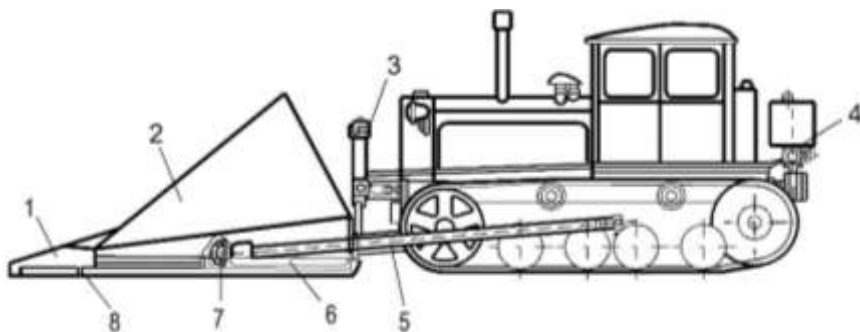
Кусторез – для корчевки или срезки кустарниковой растительности:
